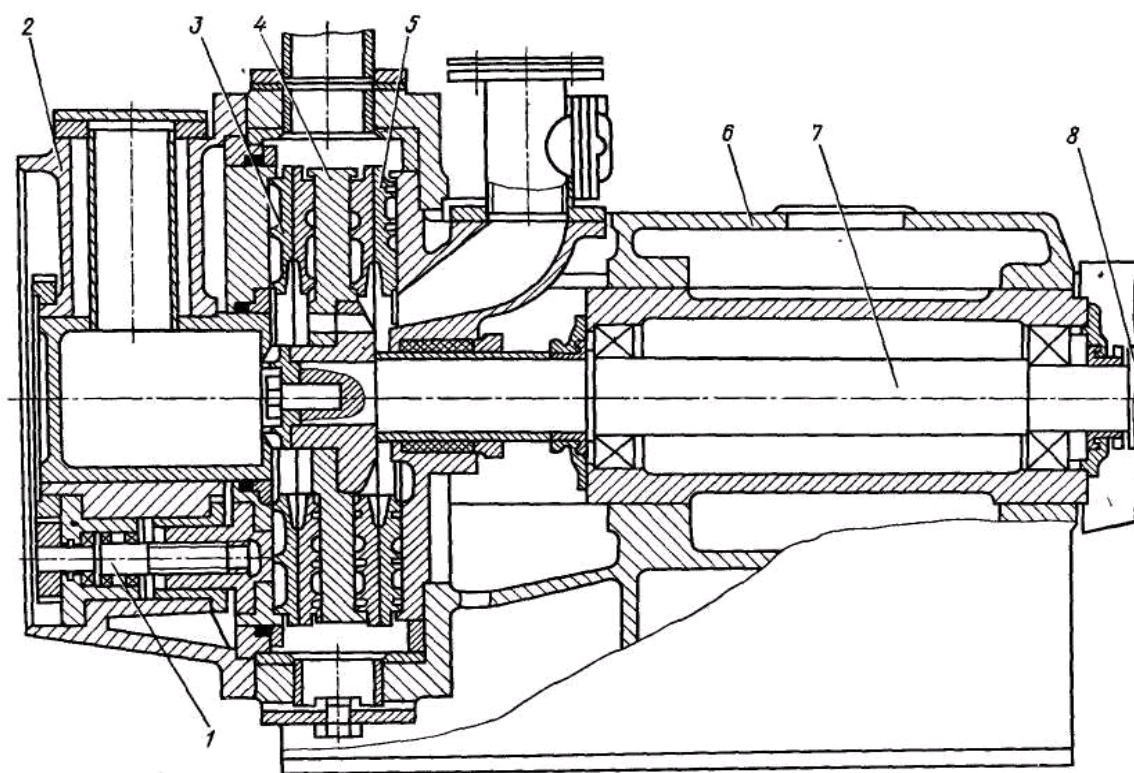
Сдвоенная мельница: 1 - винтовая пара; 2 - крышка камеры; 3 - статор; 4 - диск ротора; 5 - гарнитура размалывающая; 6 - станина; 7 - ротор; 8 - муфта
